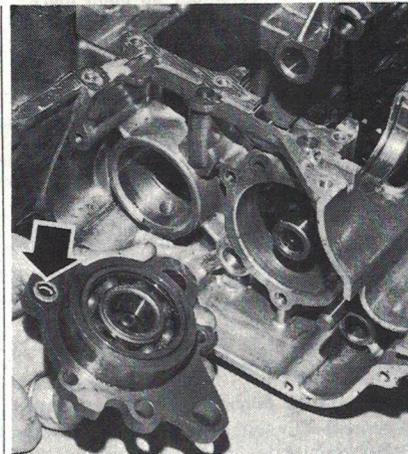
Plaque de passage d'huile d'arbre secondaire et son joint torique (Photo RMT)
